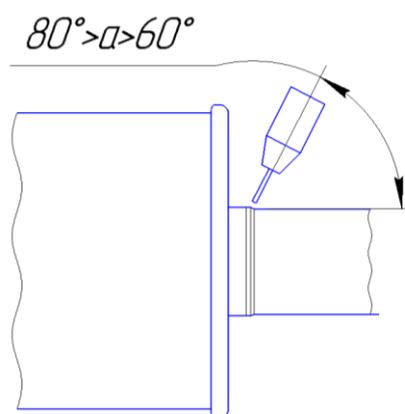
Сварка основного глушителя с трубой задней.=
